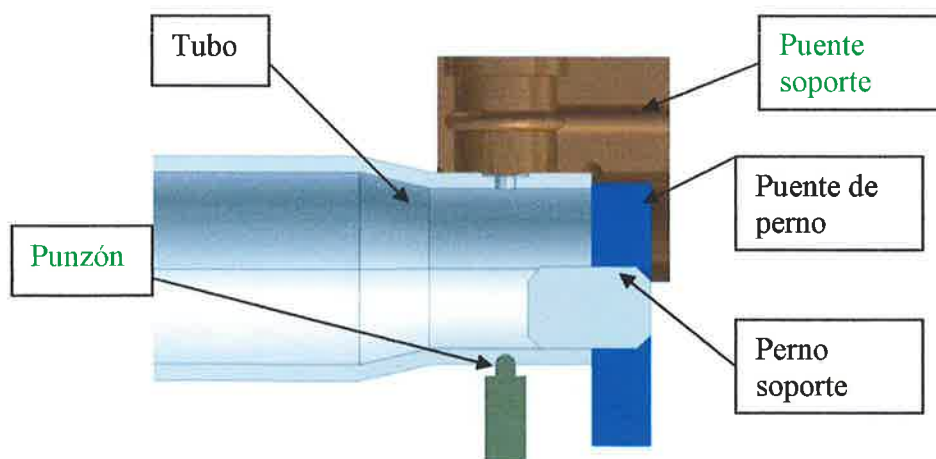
Partes principales seccionadas que componen el proceso dimpling.
